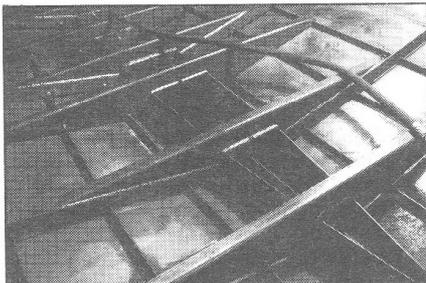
Varangues en tôles pliées sur construction artisanale.
